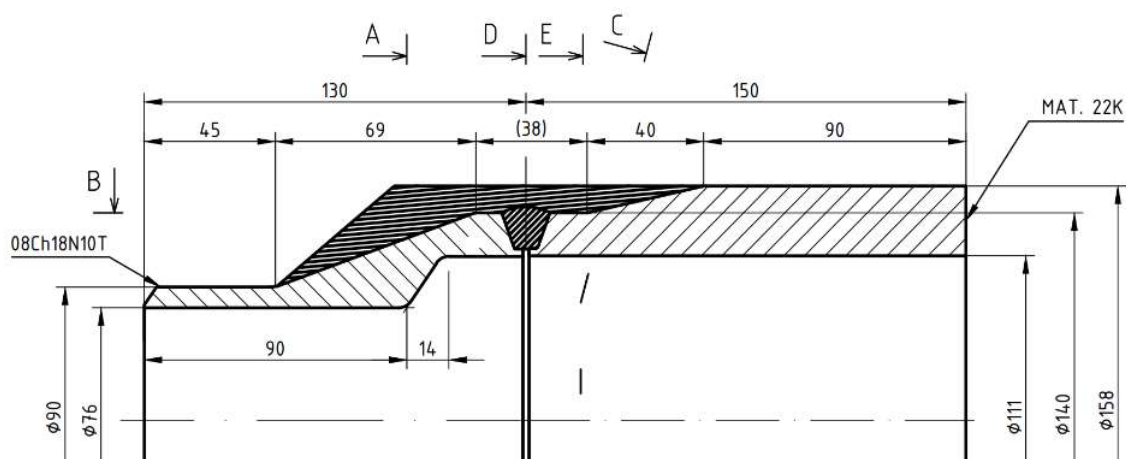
Princip technologického postupu Weld Overlay (přepracováno) [70]
